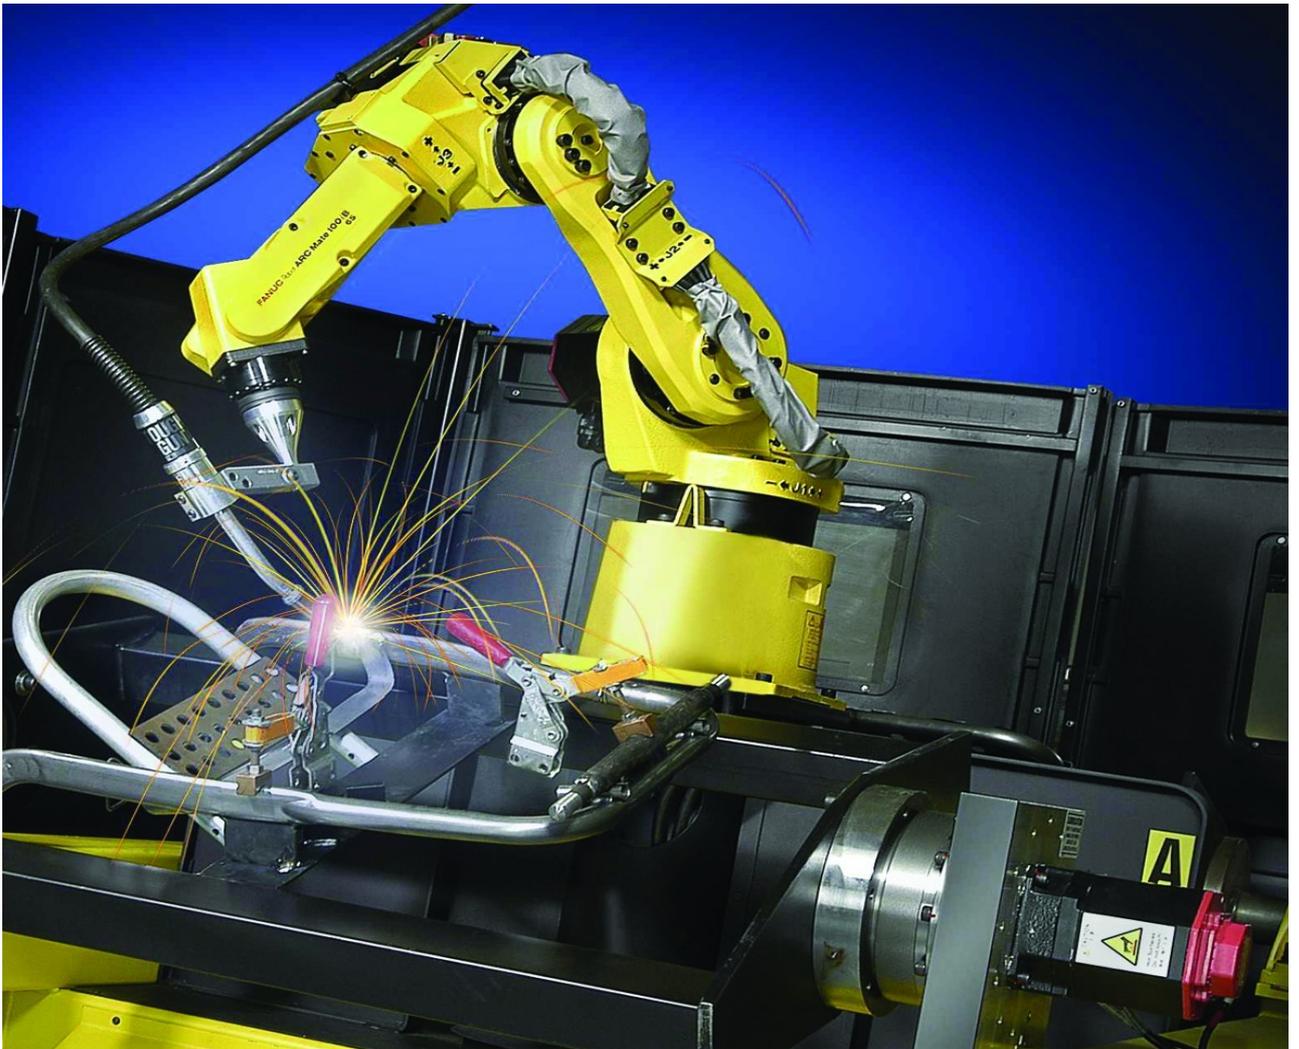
Автоматический сварочный аппарат в работе
